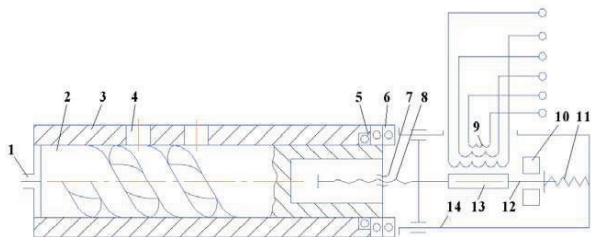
Ступенчатый дроссель: 1, 5, 6 - радиально-упорный и упорные подшипники; 2 - плунжер; 3 - корпус; 4 - радиальные отверстия подвода и отвода рабочего тела; 7 - гайка; 8 - ходовой винт; 9 - катушка электромагнита; 10 - статор; 11 - пружина; 12 - толкатель; 13 - якорь; 14 - стакан
